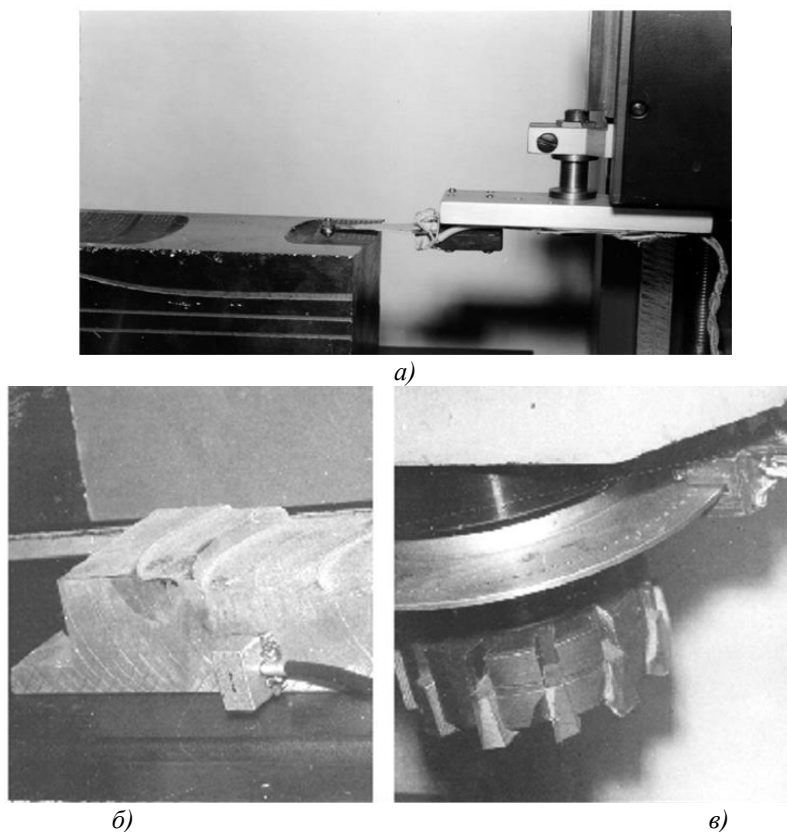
Элементы установки для замера шероховатости и получения массива виброускорений:
